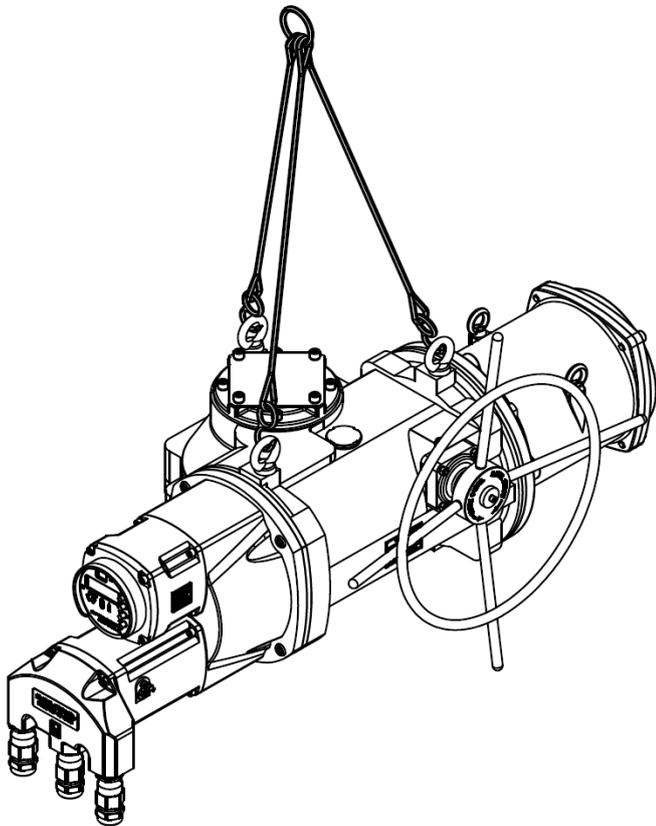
г – Схема строповки привода конструктивной схемы 43
